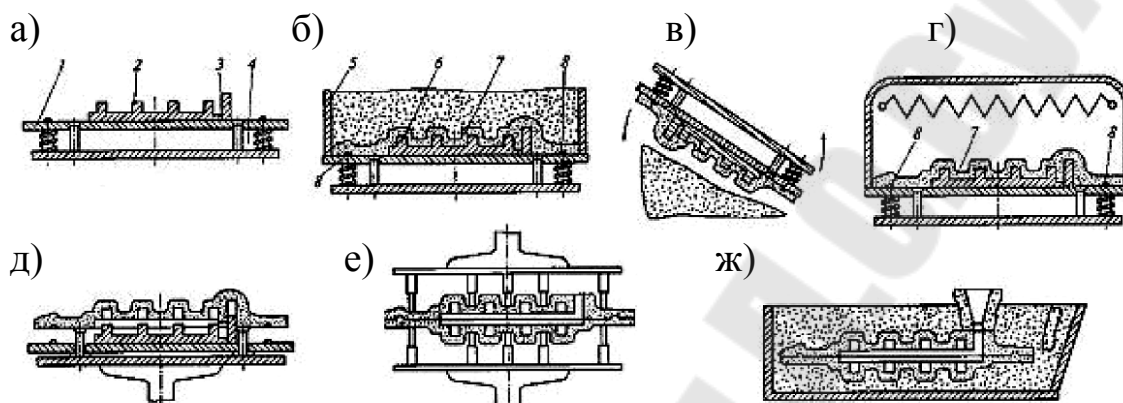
Схема технологического процесса изготовления оболочковых форм: а – подготовка модельной оснастки; б – засыпка модельной плиты смесью; в – удаление излишков смеси; г – окончательное затвердевание оболочки в печи; д – съем оболочковой полуформы с модельной плиты; е – склеивание оболочковых полуформ; ж – подготовка формы к заливке; 1 – модельная плита; 2 – модель отливки; 3 – литниковая система; 4 – плита толкателей; 5 – бункер со смесью; 6 – смесь; 7 – формирующая оболочка; 8 – элементы центрирования оболочковой полуформы при будущей сборке.
